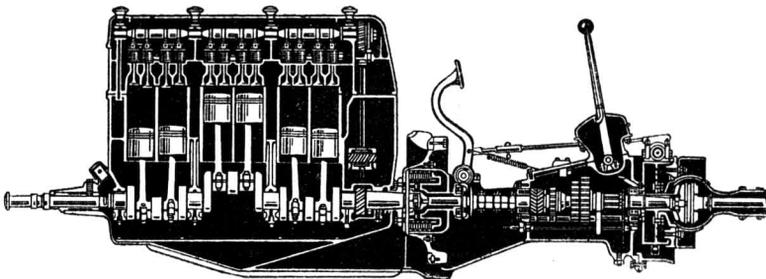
Schnitt durch einen Sechs-Zylinder-Ottomotor mit obenliegender Nockenwelle, Kupplung, Getriebe und Kreuzgelenk
